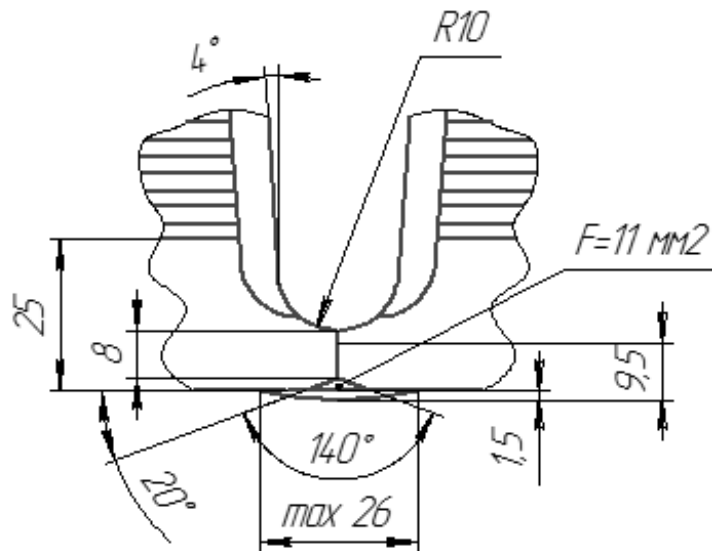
Геометрія для кореневої ділянки шва
